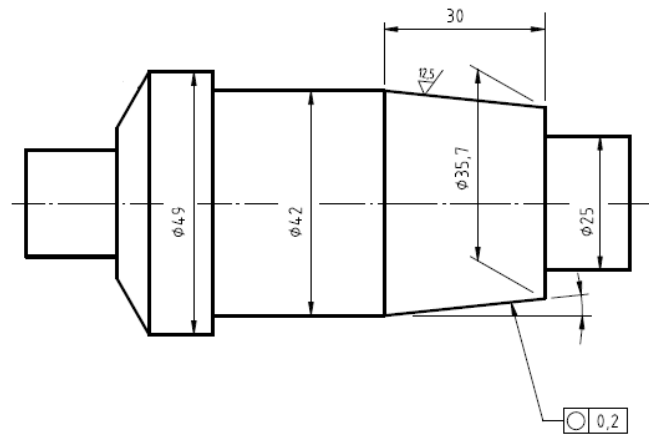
Eixo cilíndrico e cônico com rebaixos – planificado
